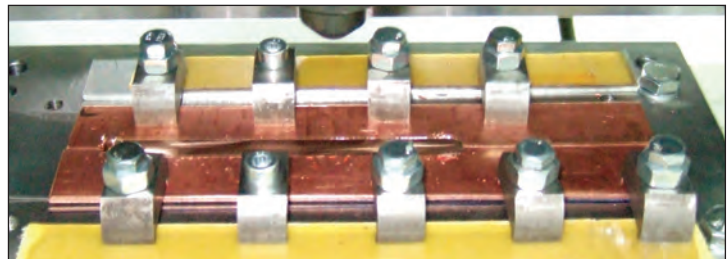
Медные пластины после сварки трением с перемешиванием
